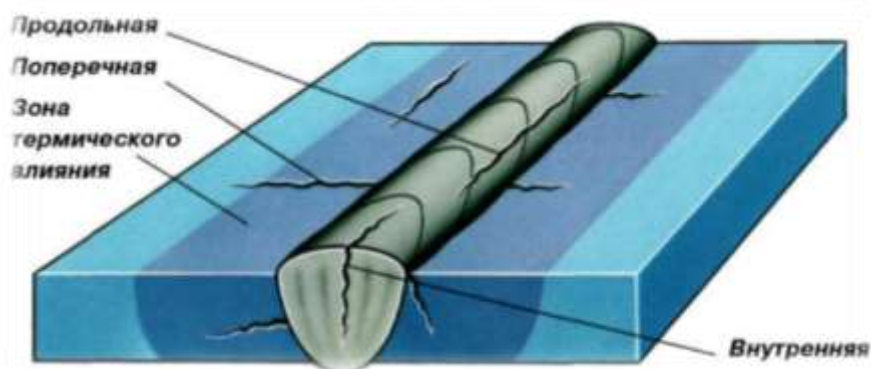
Дефекты сварного шва по типу трещин
